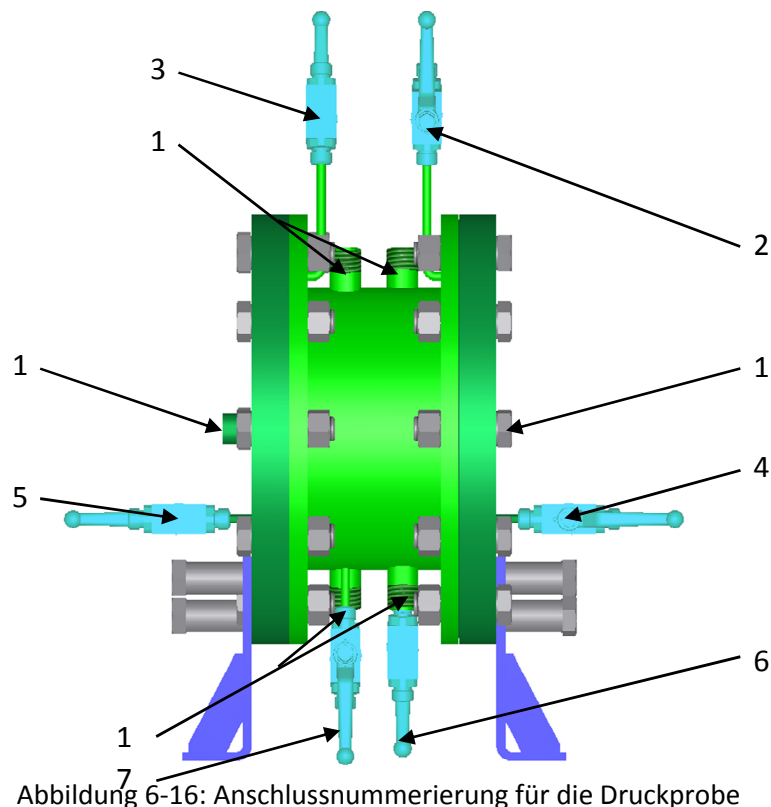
Anschlussnummerierung für die Druckprobe
